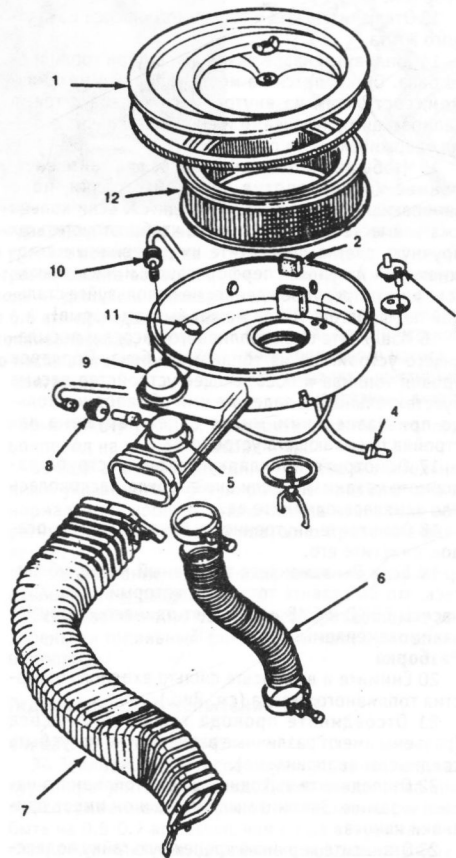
б Сборка воздухоочистителя — покомпонентное изображение (шестицилиндровый V-образный двигатель)
